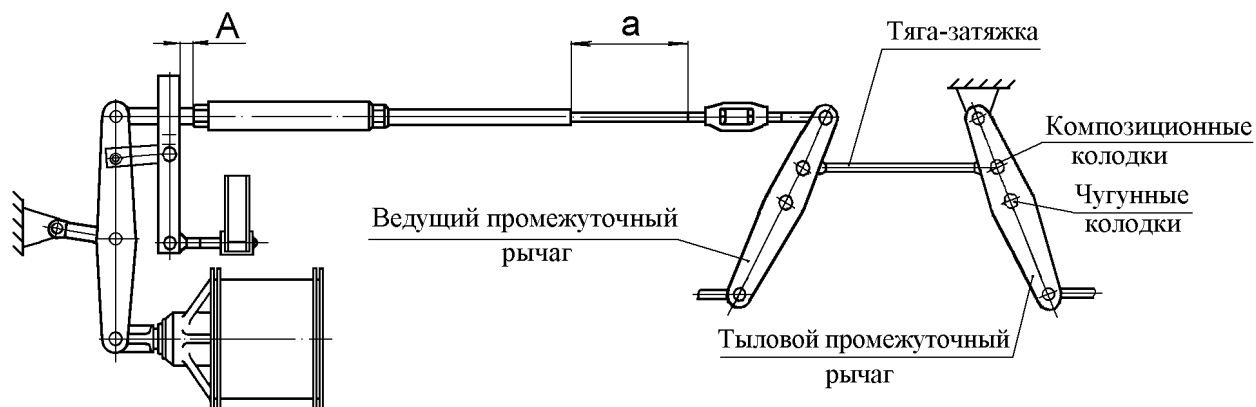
Схема несимметричной тормозной рычажной передачи вагона-хоппера для перевозки окатышей (см. рис. 9)
